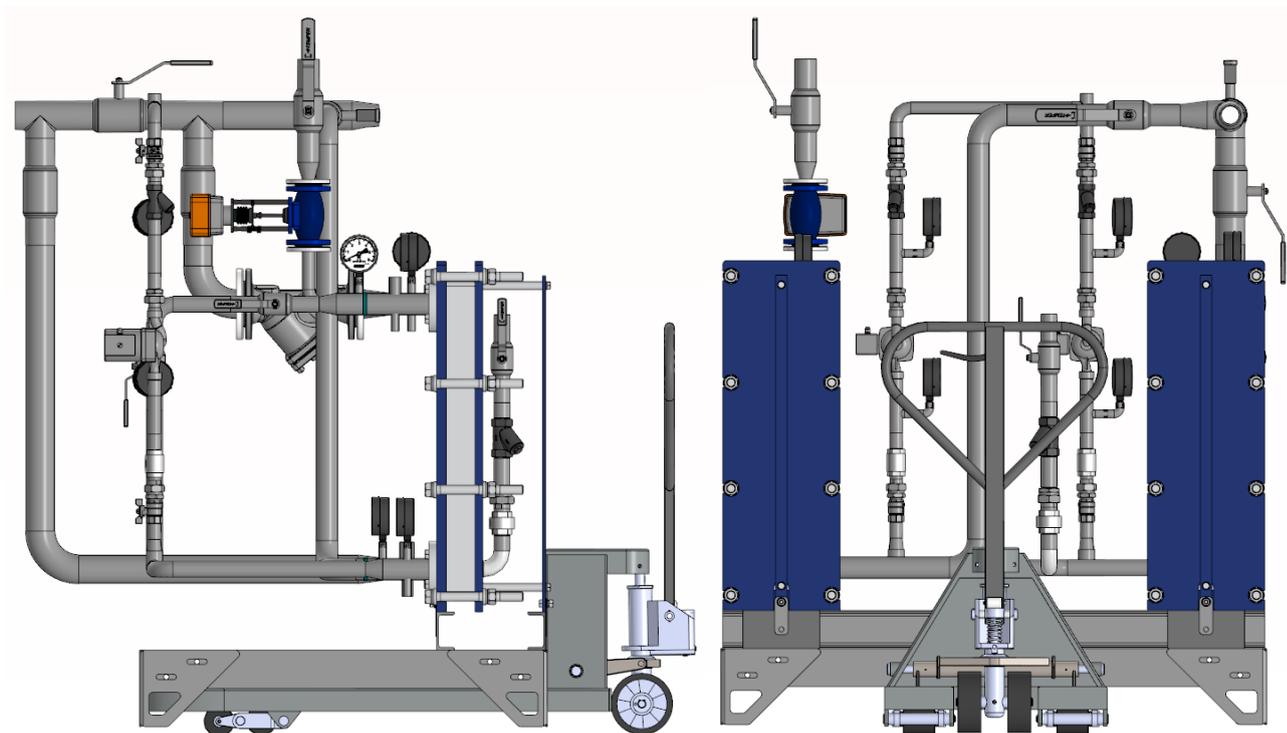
Схема транспортировки блока с помощью вилочной тележки
